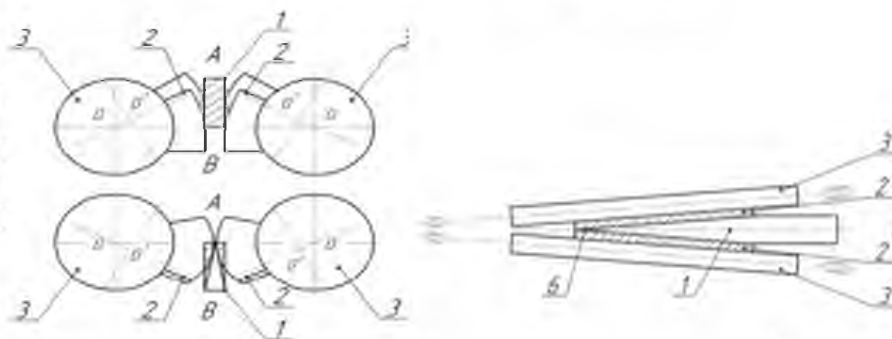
Схема одночасної прокатки клинка у поздовжньому (а) та поперечному (б) напрямках: 1 – заготовка ножа, 2 – деформуючі елементи, 3 – система валів.
